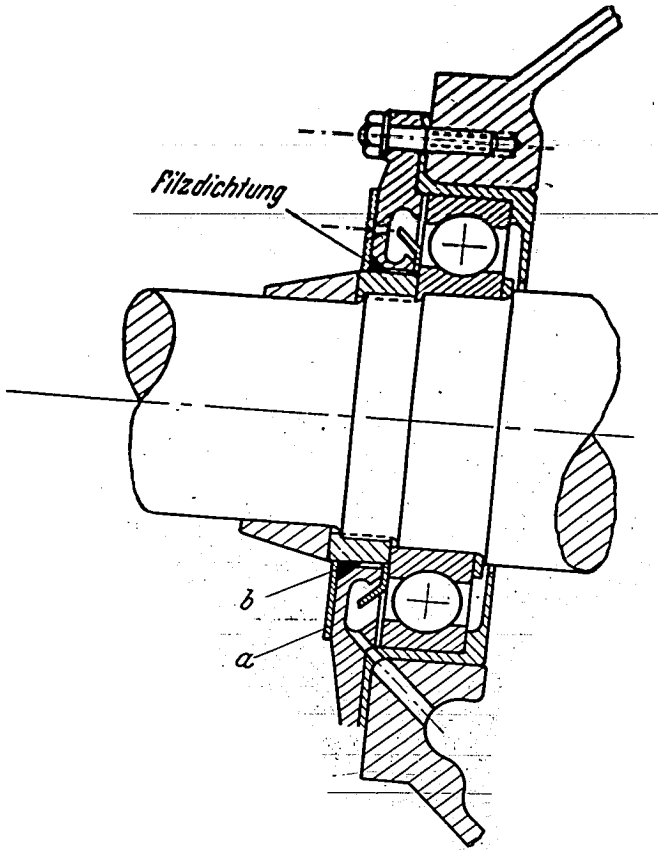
Schnitt durch das vordere Lager im BMW 132.
